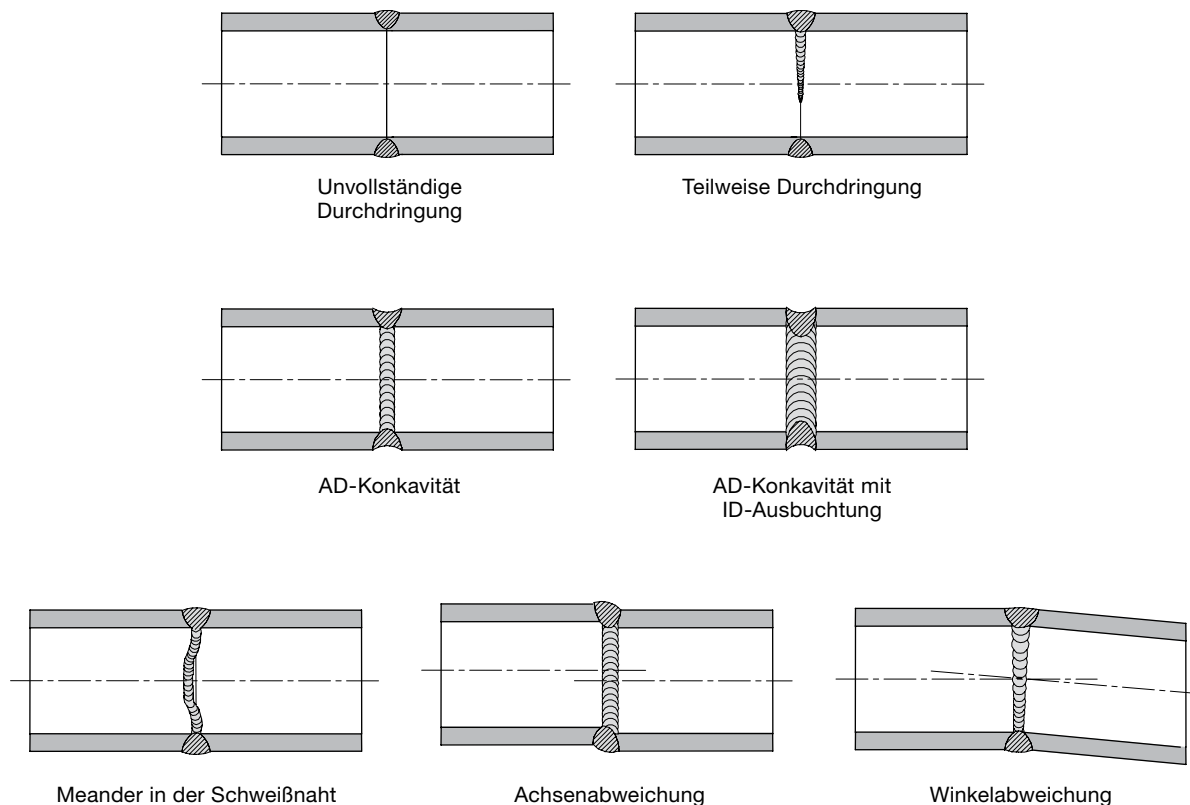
Typische Schweißunregelmäßigkeiten
